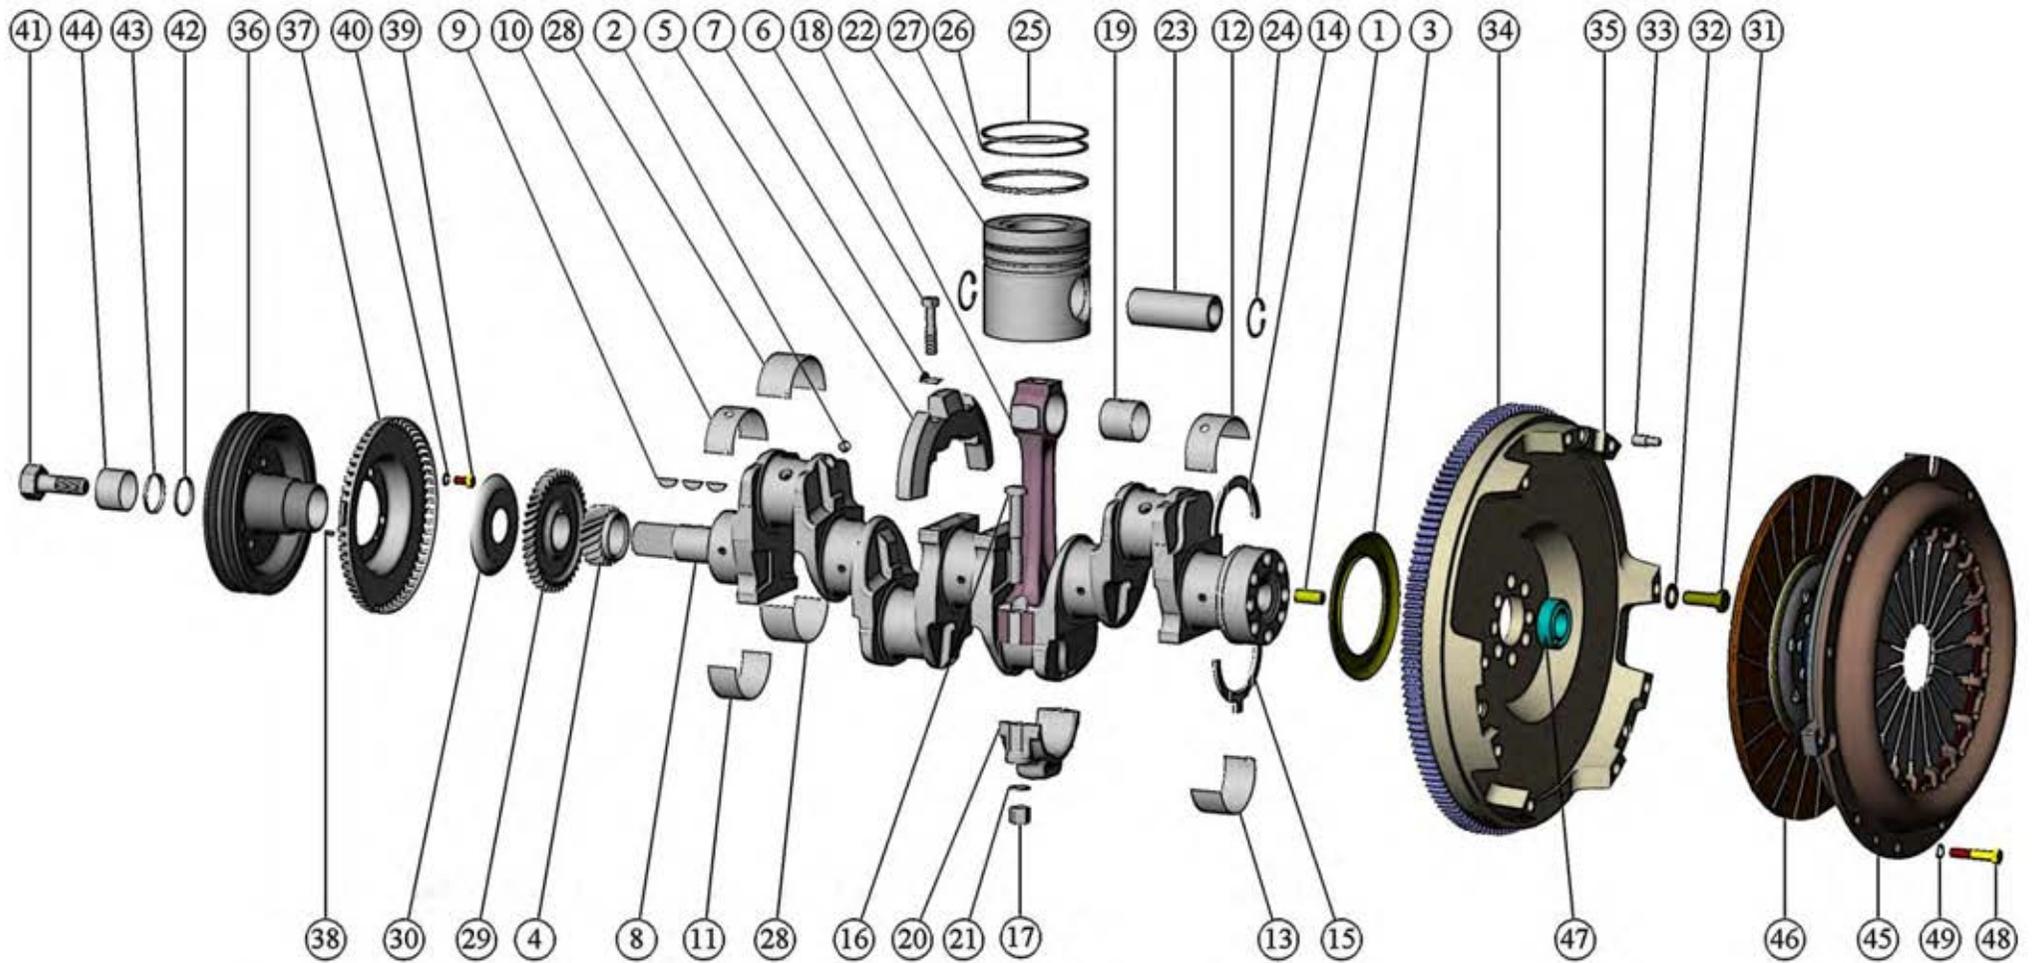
Кривошипно-шатунный механизм. Установка маховика. Установка шкива. Установка муфты сцепления.
